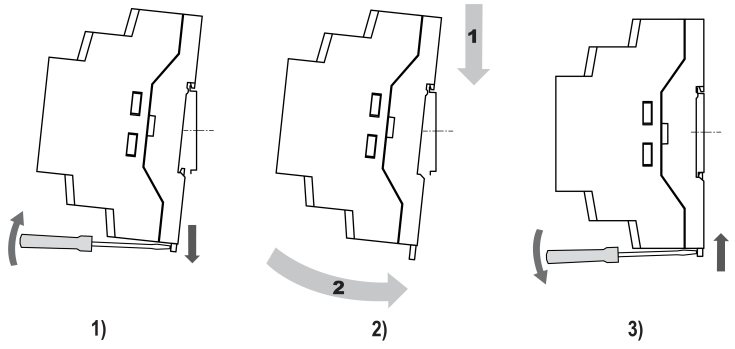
Монтаж прибора с креплением на DIN-рейку
